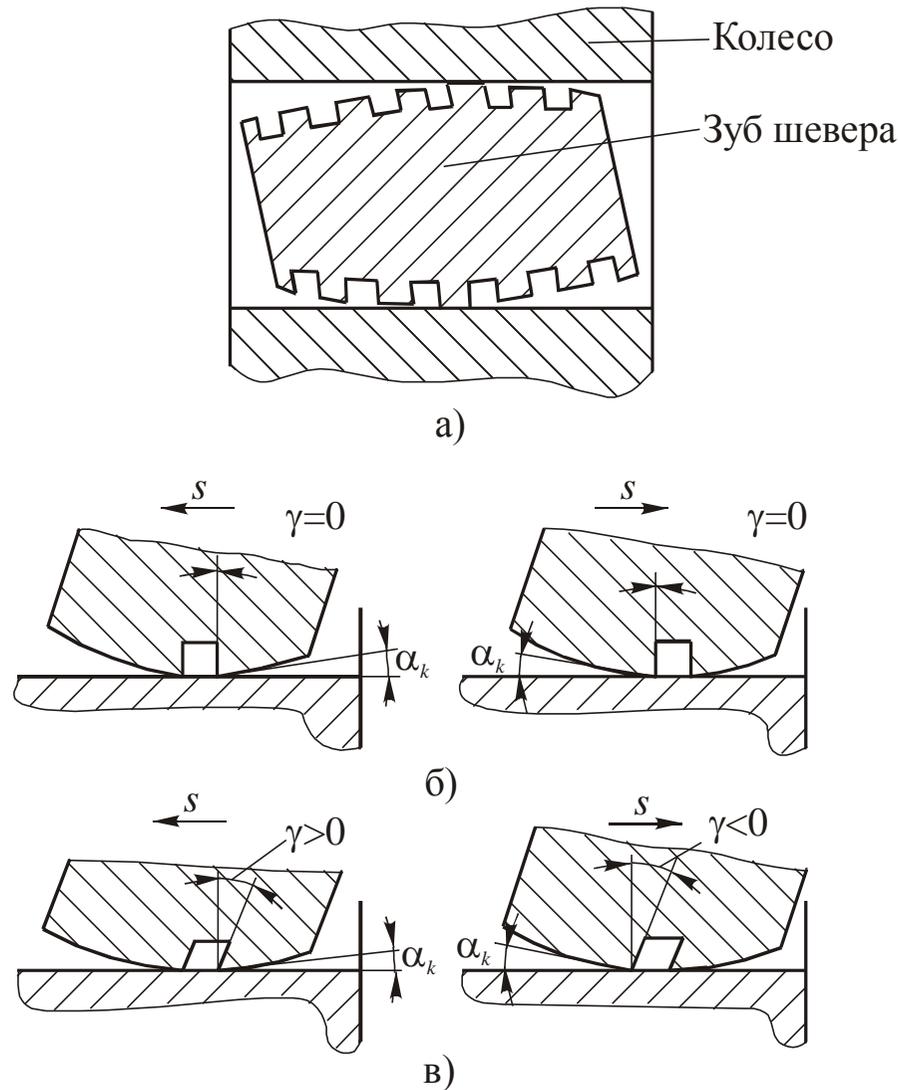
Контакт зубьев шевера и колеса: *a* – развертка сечения зуба шевера делительным цилиндром во впадине зуба колеса; *б* – передний и задний углы в случае, когда канавки перпендикулярны направлению зуба; *в* – канавки параллельны торцу зуба
